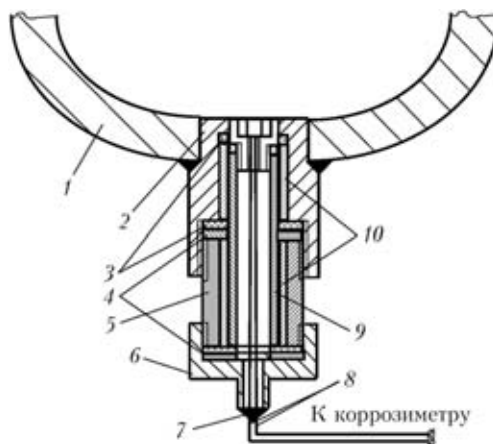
Схема двухэлектродного ПП для измерения скорости коррозии, смонтированного на нефтепроводе: 1 — трубопровод; 2 — монтажный патрубок; 3 — шайба-уплотнитель; 4 — шайба металлическая; 5 — прижимная гайка; 6 — крышка; 7 — герметик; 8 — токоотводы; 9 — труба-штанга; 10 — втулка-уплотнитель
